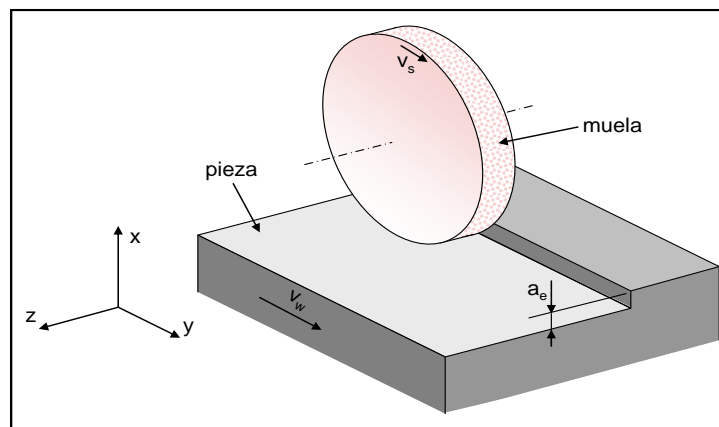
Rectificado plano. Fuente: Escuela Técnica Superior de Ingeniería
